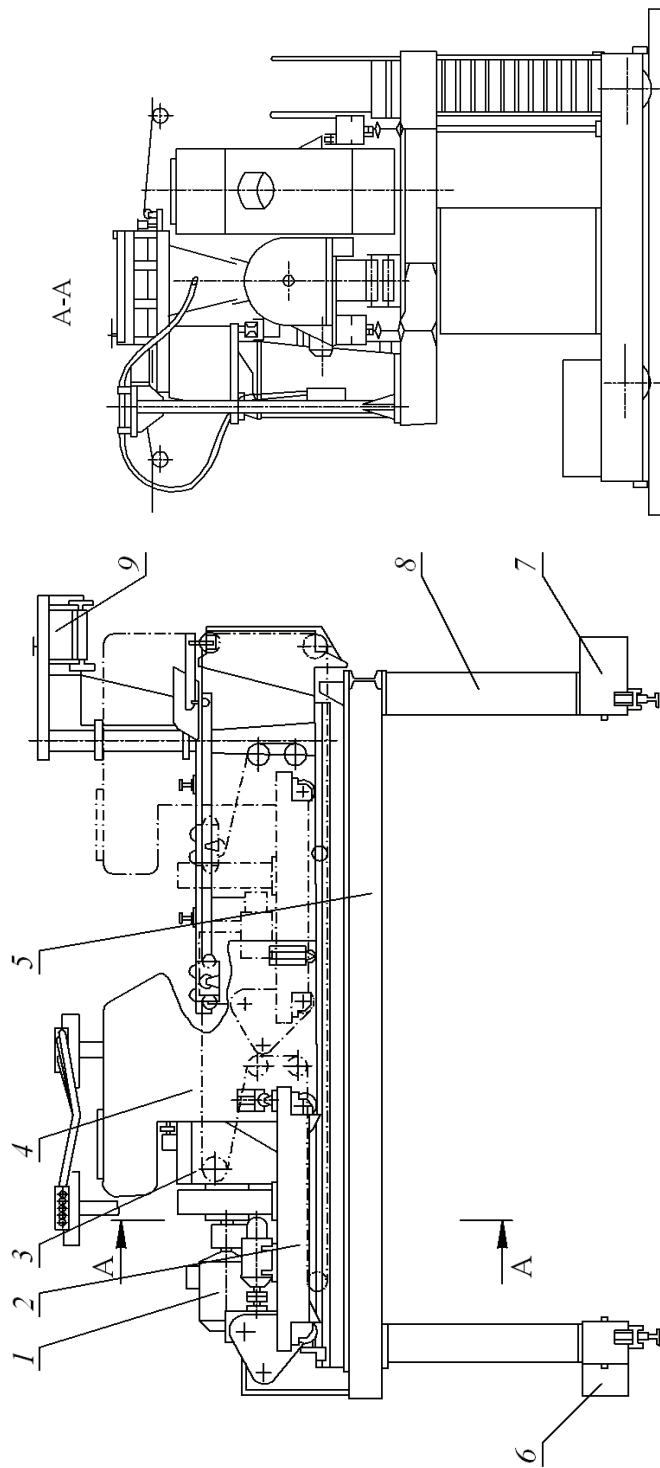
Общий вид пескомета модели 24512М: 1 – головка пескомета; 2 – тележка; 3 – механизм подсыпки; 4 – кабина; 5 – мост; 6 – площадка левая; 7 – площадка правая; 8 – опора; 9 – механизм разгрузки
